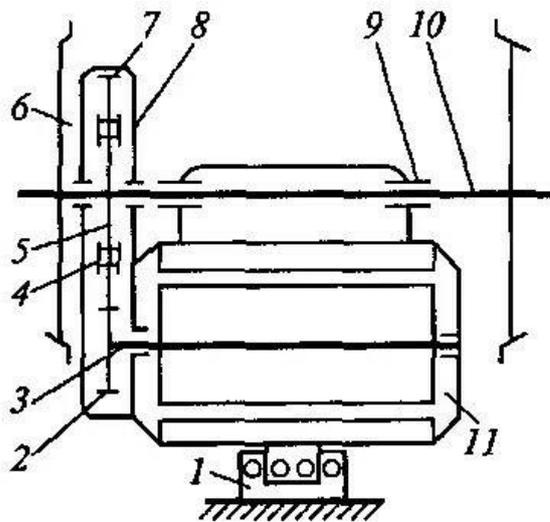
Схема опорно-осевой подвески тягового электродвигателя: 1 - пружинный комплект на раме тележки; 2 - зубчатое колесо якоря ТЭД; 3 - вал якоря ТЭД; 4 - резинометаллические втулки зубчатого колеса; 5 - ступица зубчатого колеса; 6 - колесо колесной пары; 7 - зубчатый венец; 8 - кожух тягового редуктора; 9 - моторно-осевые подшипники; 10 - ось колесной пары; 11 - ТЭД
